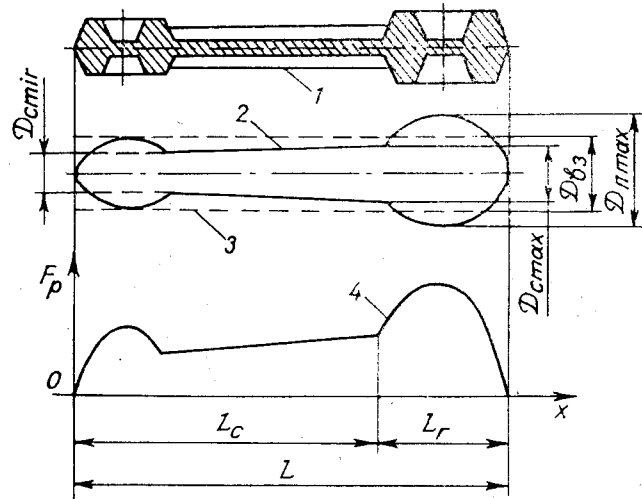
Схема побудови розрахункової заготовки: 1 — ковanka; 2 — розрахункова заготовка; 3 — вихідна заготовка; 4 — еюра перетинів.
